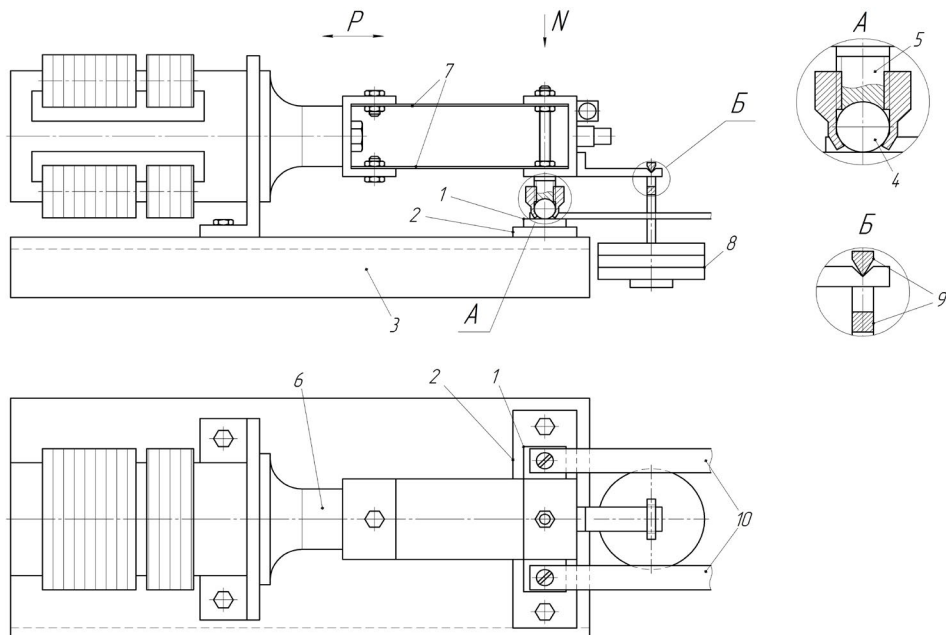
Конструкция стенда. Обозначения: 1 — образец; 2 — диэлектрическая подложка; 3 — основание; 4 — индентор; 5 — держатель индентора; 6 — магнитострикционный преобразователь; 7 — подвеска индентора; 8 — грузы; 9 — подвеска грузов; 10 — токоведущие шины.
